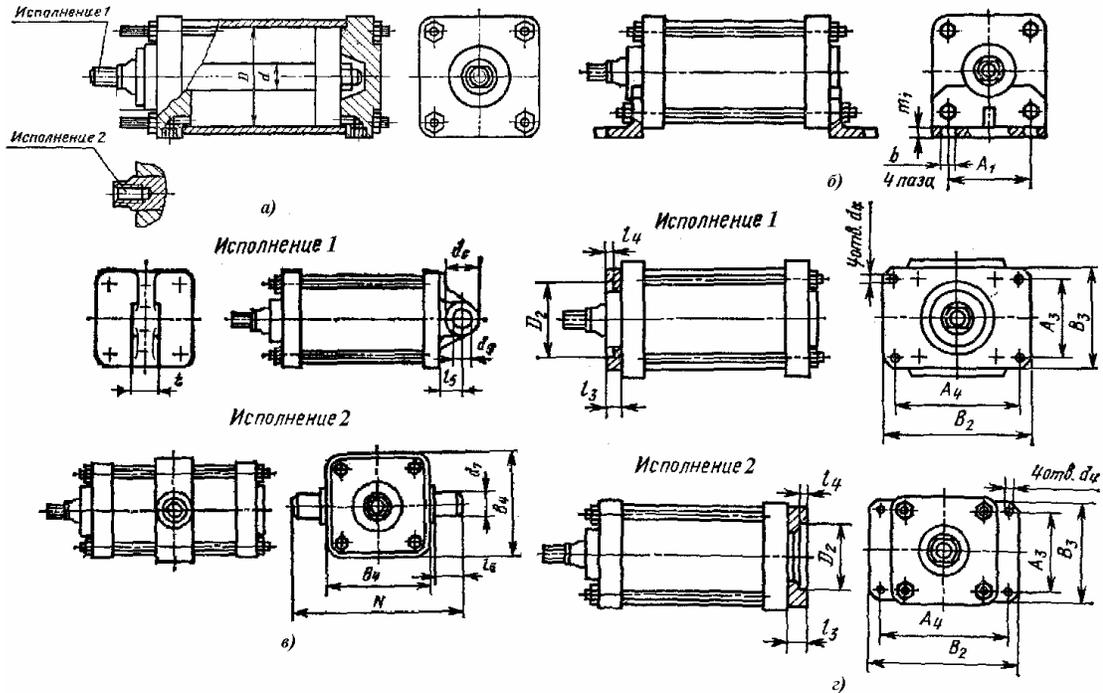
Стационарные пневмоцилиндры (а- с удлиненными стяжками; б – с лапками; в - с шарнирным креплением; г - с шарнирным креплением)
